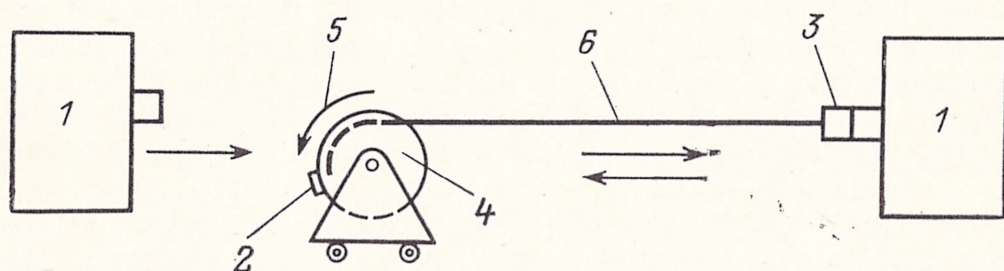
Схема намотки кабельного ствола на барабан.
